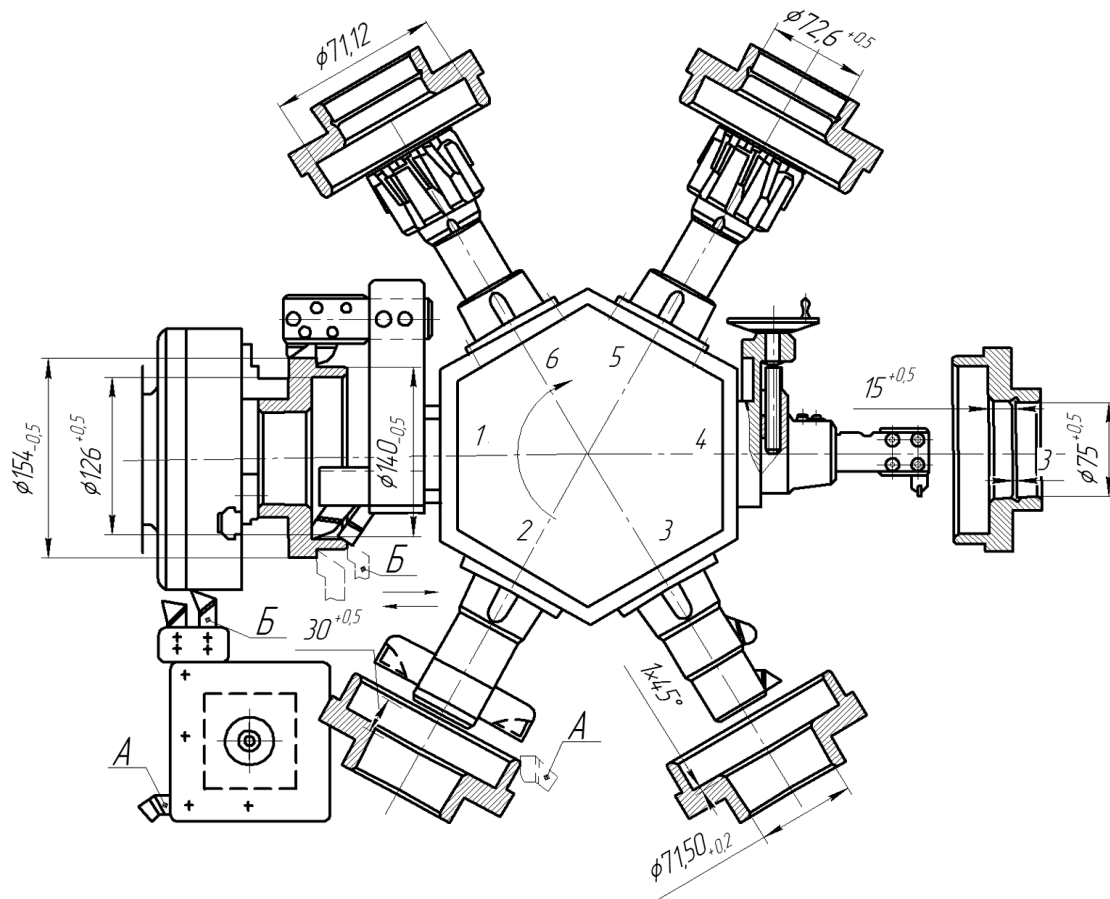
Технологічна наладка оброблення зубчастого колеса на токарно-револьверному верстаті
